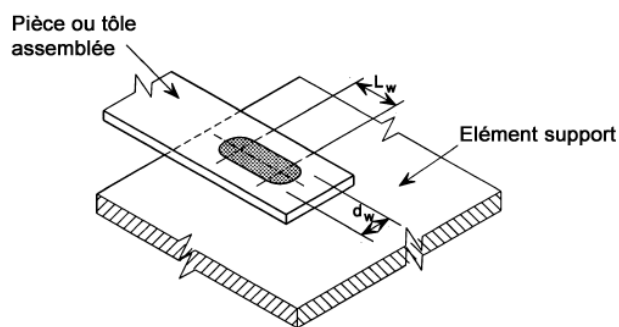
Soudure bouchon à l'arc oblongue
